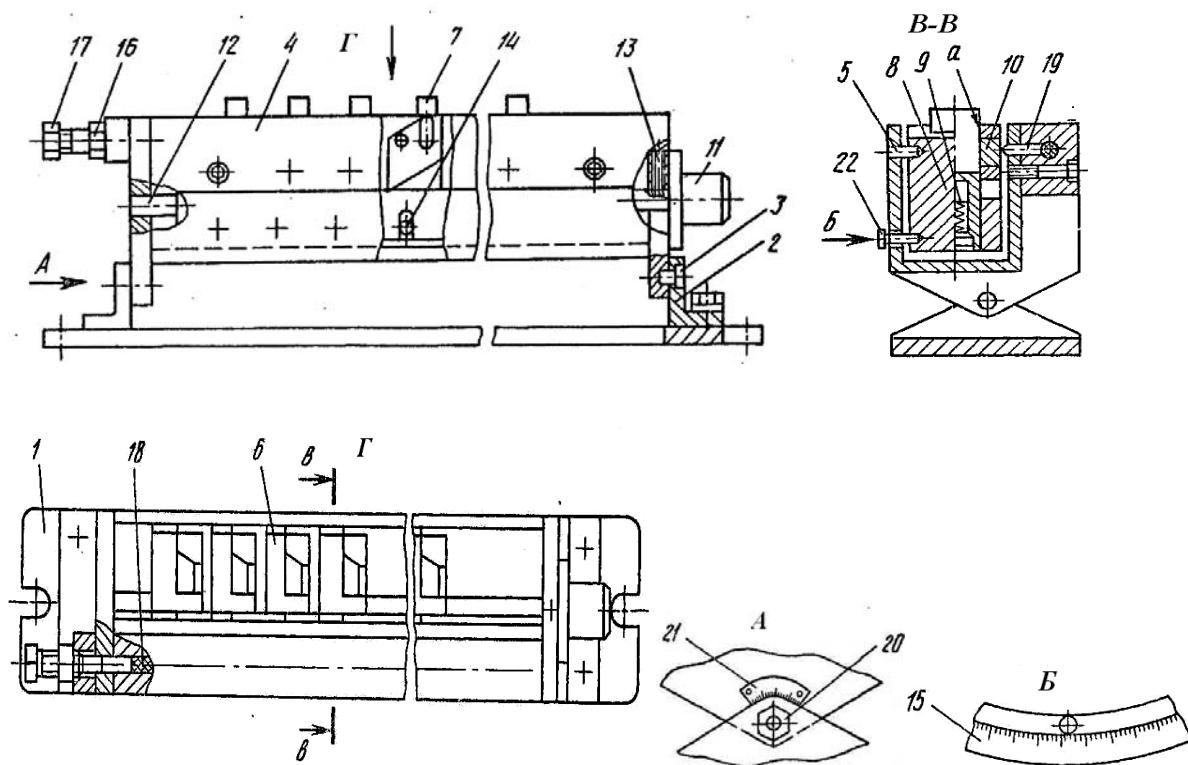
Эскиз приспособления для заточки пластин сборного металлорежущего инструмента
